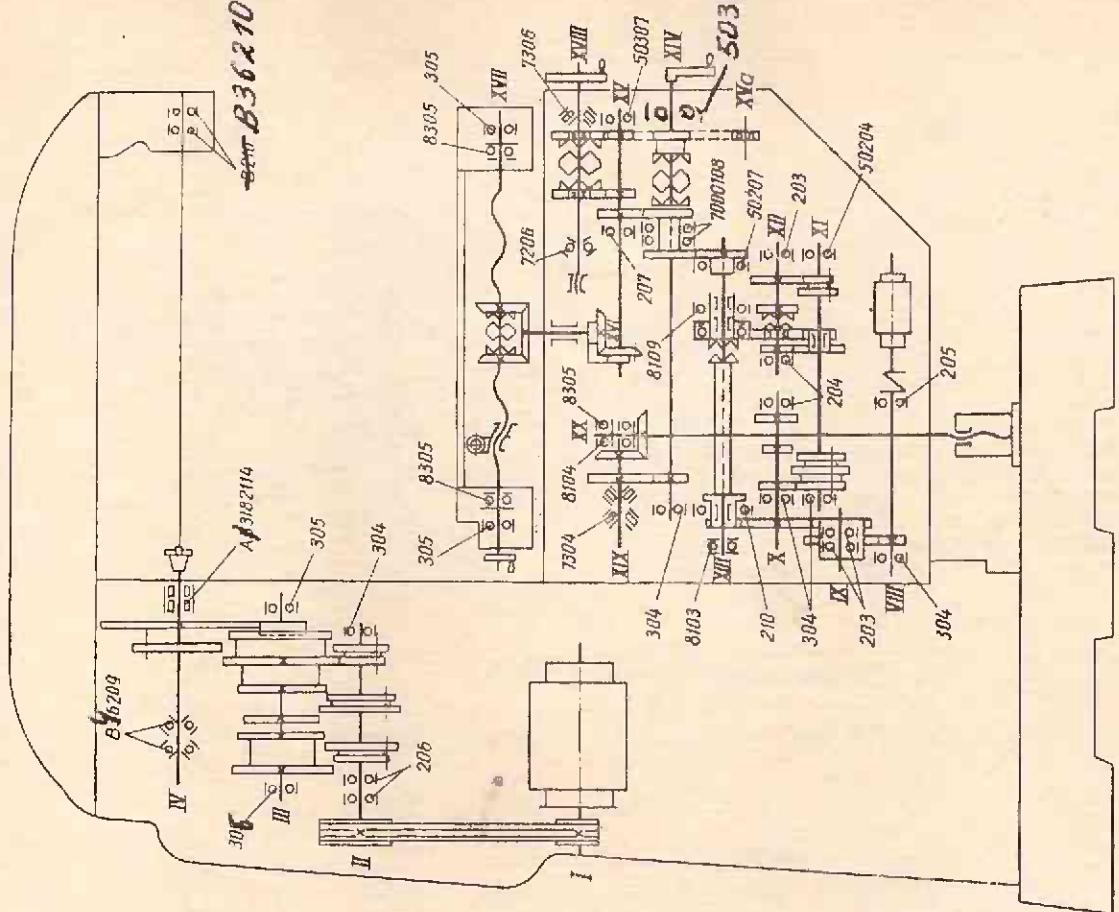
Схема расположения подшипников качения станков 6Н80 и 6Н180
